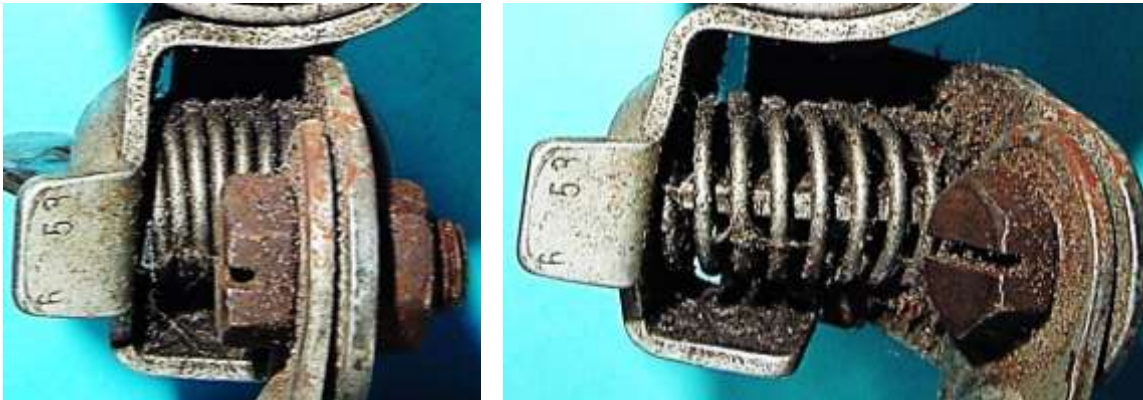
Auf Druck beanspruchte Feder in der Kippvorrichtung
